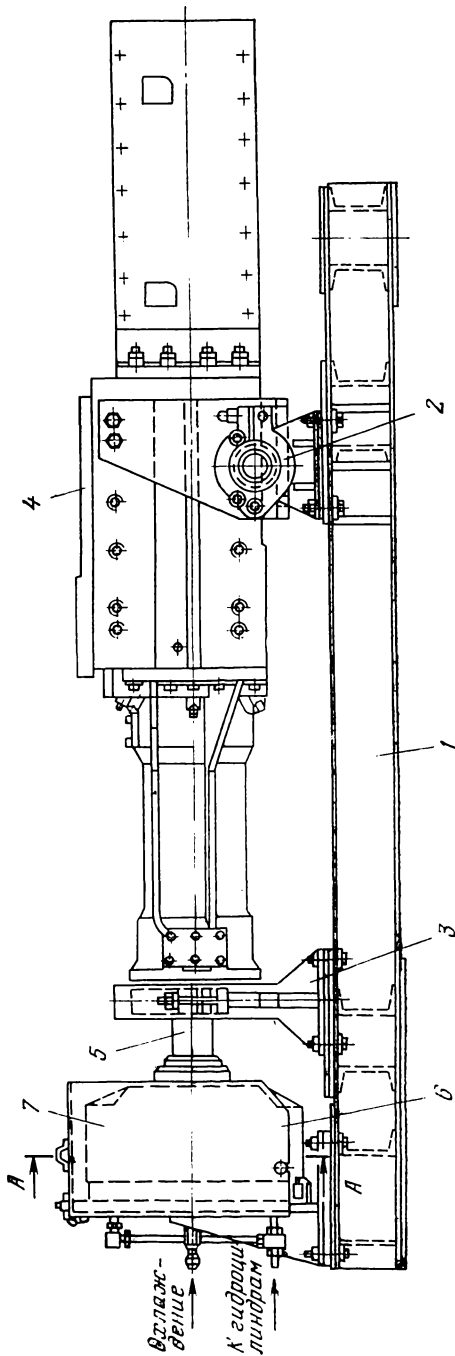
Стенд для испытания рабочего органа проходческого комбайна ПК-3М
